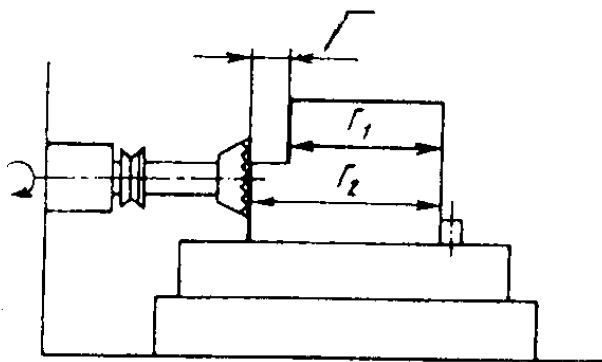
Схема получения размера между поверхностями, обработанными за один установ заготовки и режущего инструмента
